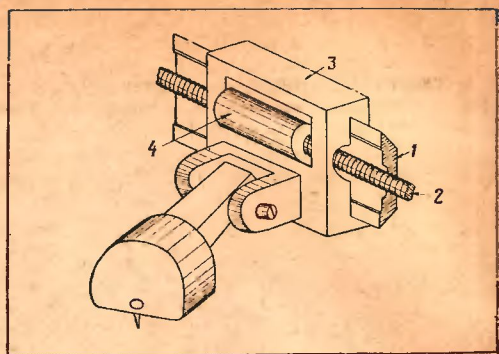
Направляющая в виде „ласточкино-го хвоста“. 1 — неподвижная рейка; 2 — ходовой винт, 3 — ползун; 4 — ведущая гайка
